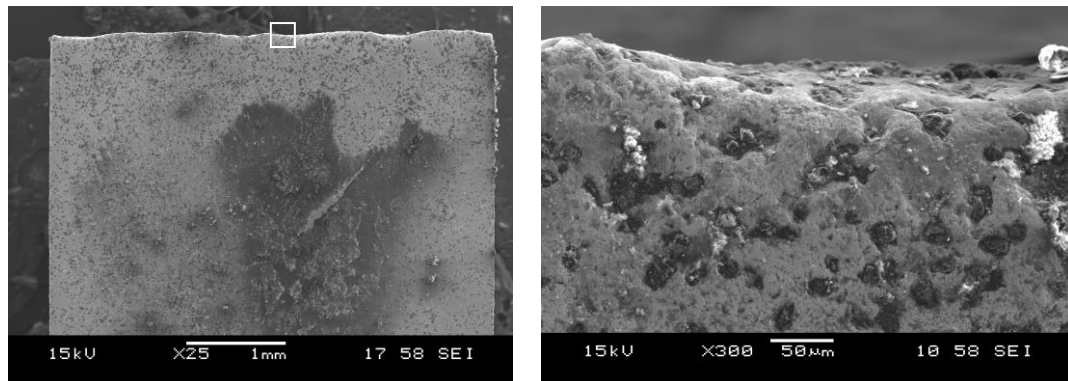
24 Refoulement de matière usinée par l'arête de coupe et frottements à l'interface surface usinée/face de dépouille [GHID\_03].
